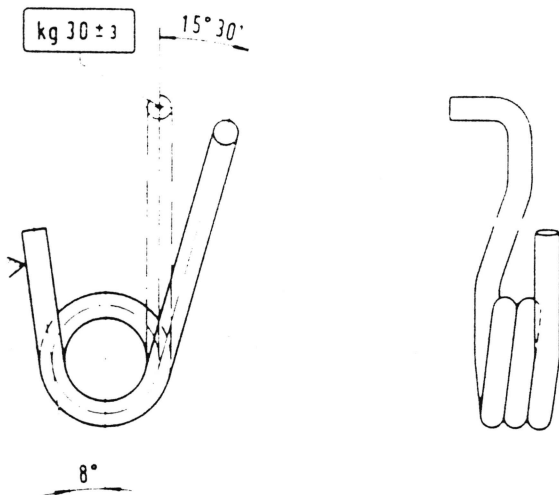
Hauptdaten zur Kontrolle der Feder für Steuerriemenspanner.
